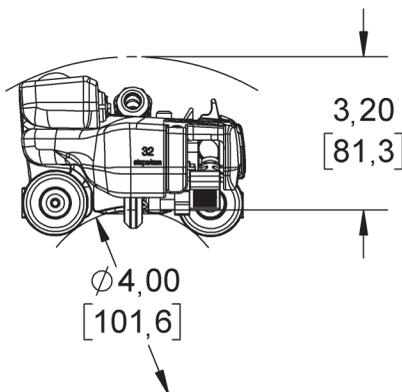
Dimensions sur la vue du côté gauche de l'HydroFORM
